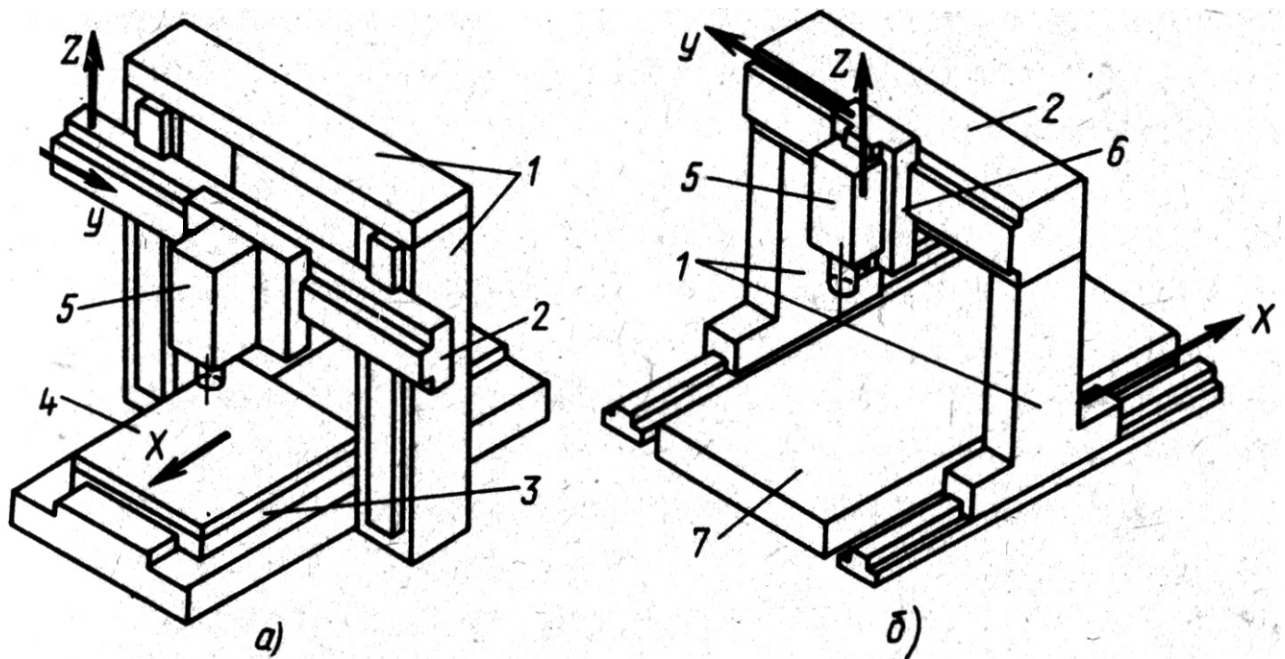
Вертикальные двухстоечные ГПМ для обработки корпусных и плоских деталей:
